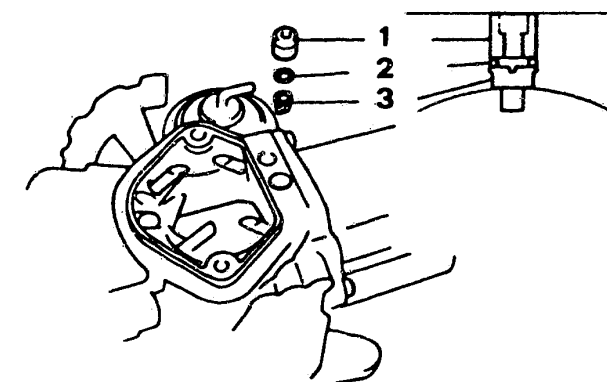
Um den Luftschieber auszubauen, ist zuerst der Zapfen (1) mit einer 4-mm-Schraube herauszuziehen, worauf sich der O-Ring (2) und das Führungsbölzchen (3) herausnehmen lassen.
